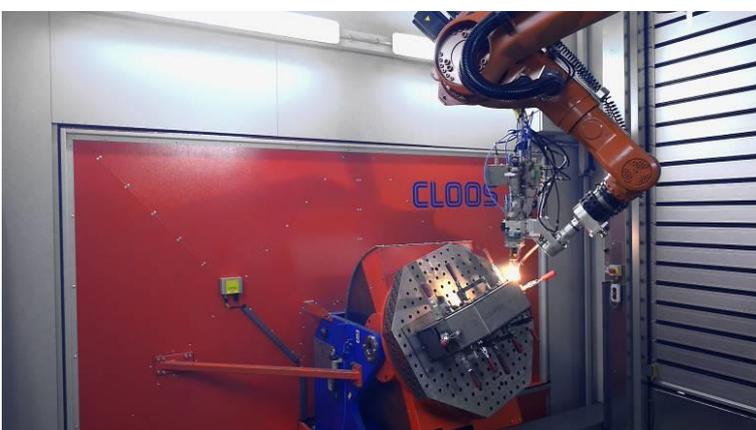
Laser Hybrid Weld zeichnet sich durch eine hohe Schweißgeschwindigkeit und optimale Nahtqualität aus.
